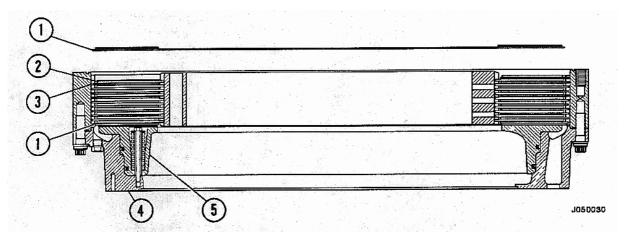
MONTAJE DEL PAQUETE DE DISCOS
